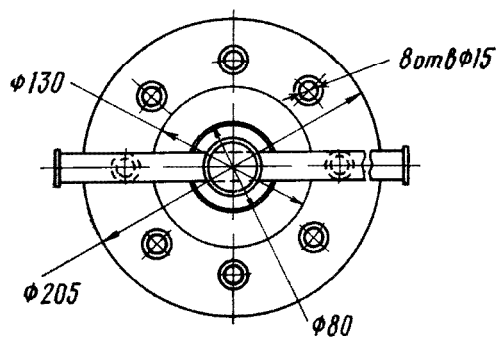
Приспособление для снятия ступицы переднего колеса:
